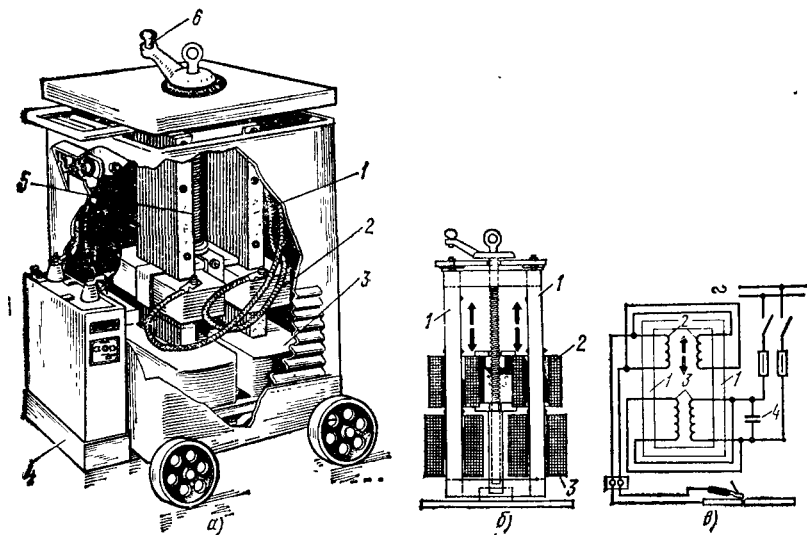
Схема сварочного трансформатора ТСК-500:
